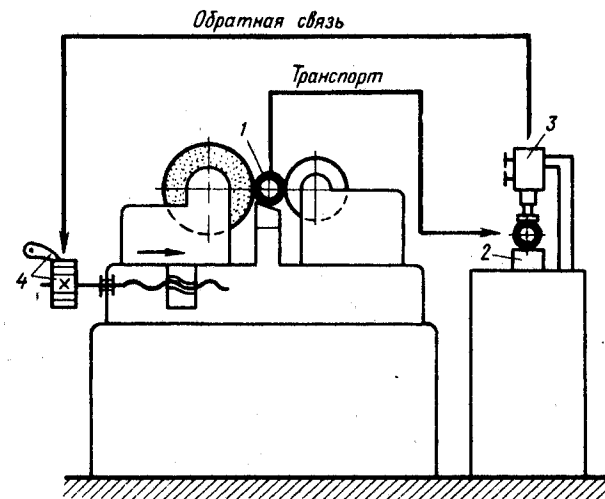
Схема подналадочной системы для бесцентрово-шлифовального станка
